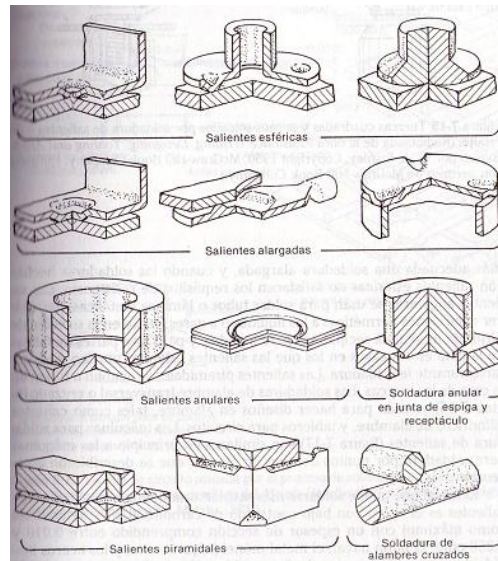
Variaciones sobre los tipos básicos de partes salientes en la soldadura de partes salientes o resaltantes
